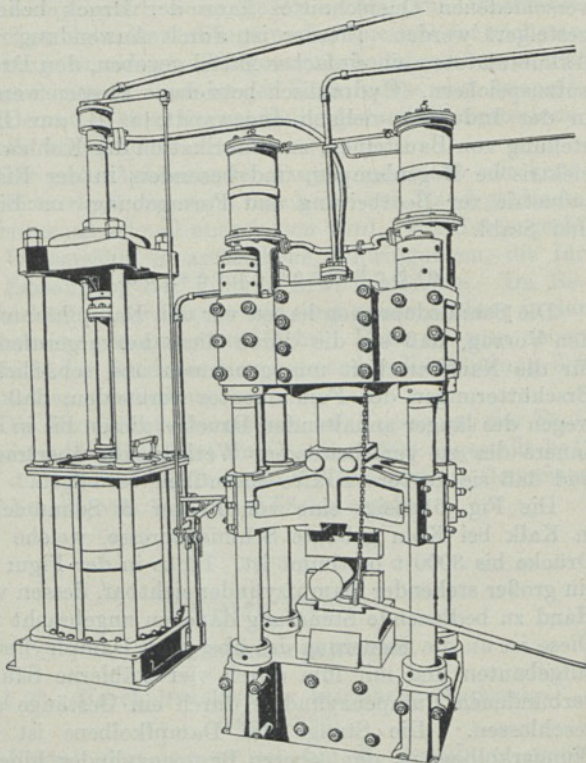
Schmiedepresse. Breuer & Schumacher, Kalk bei Köln.
